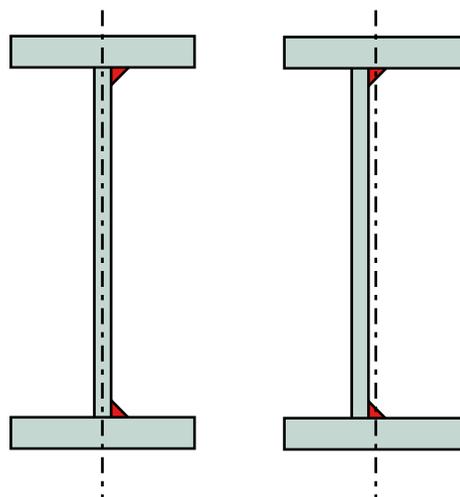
Utilizar una secuencia de soldaduras simétricas.
